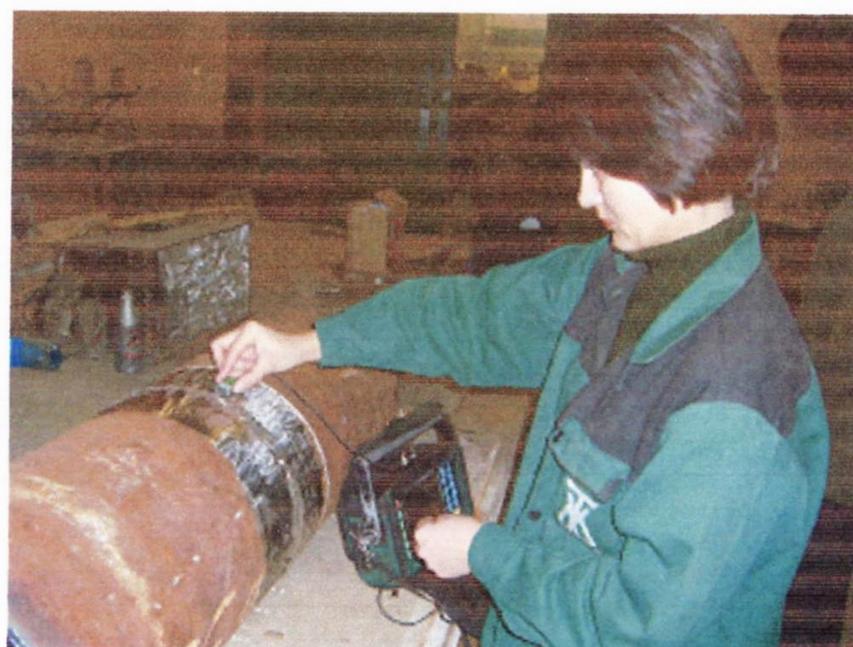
Диагностика сварного шва трубы диаметром 219мм ультразвуковым методом.
